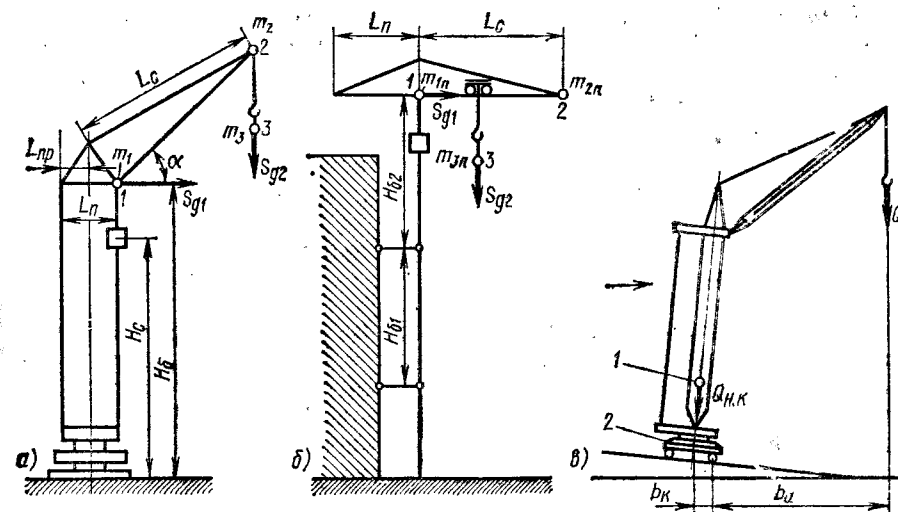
Схемы к расчету строительных башенных кранов:
